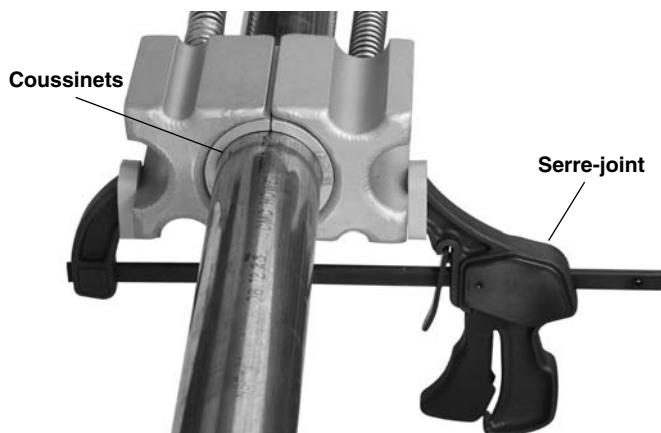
Montage des deux têtes de congélation à l'aide du serre-joint
